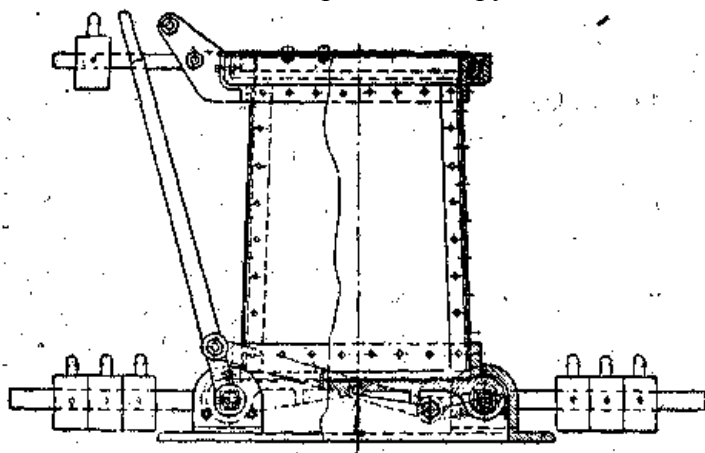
Загрузочная коробка для дров с двумя клапанами.
